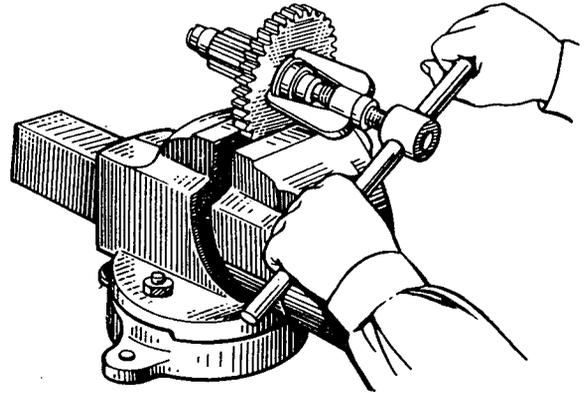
Ausbau des Innenringes des Zwischenwellenrollenlagers
